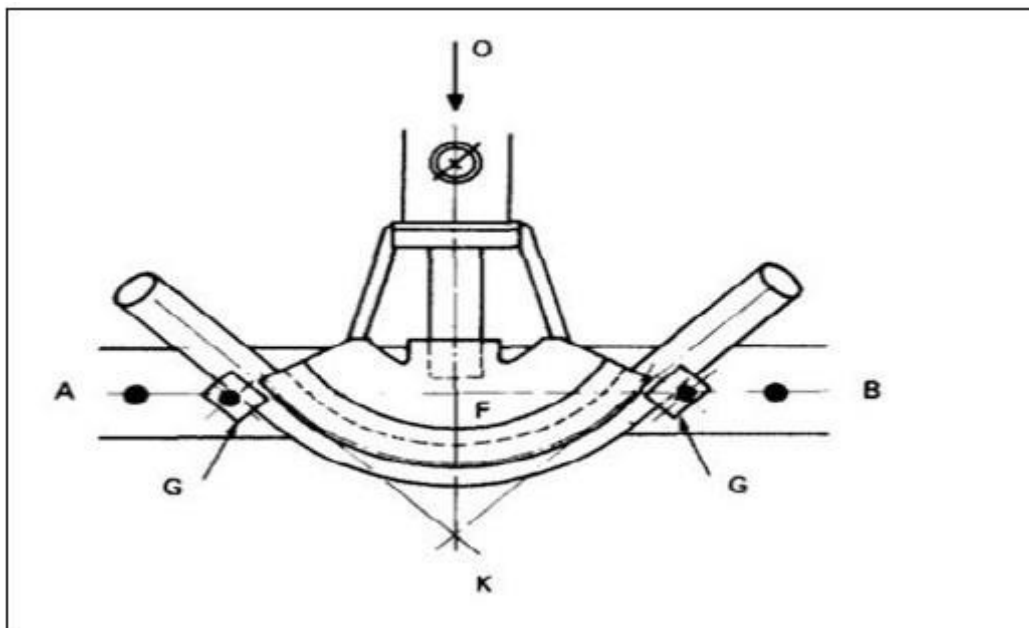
Cintrage de tube à froid par poussés. [8]
